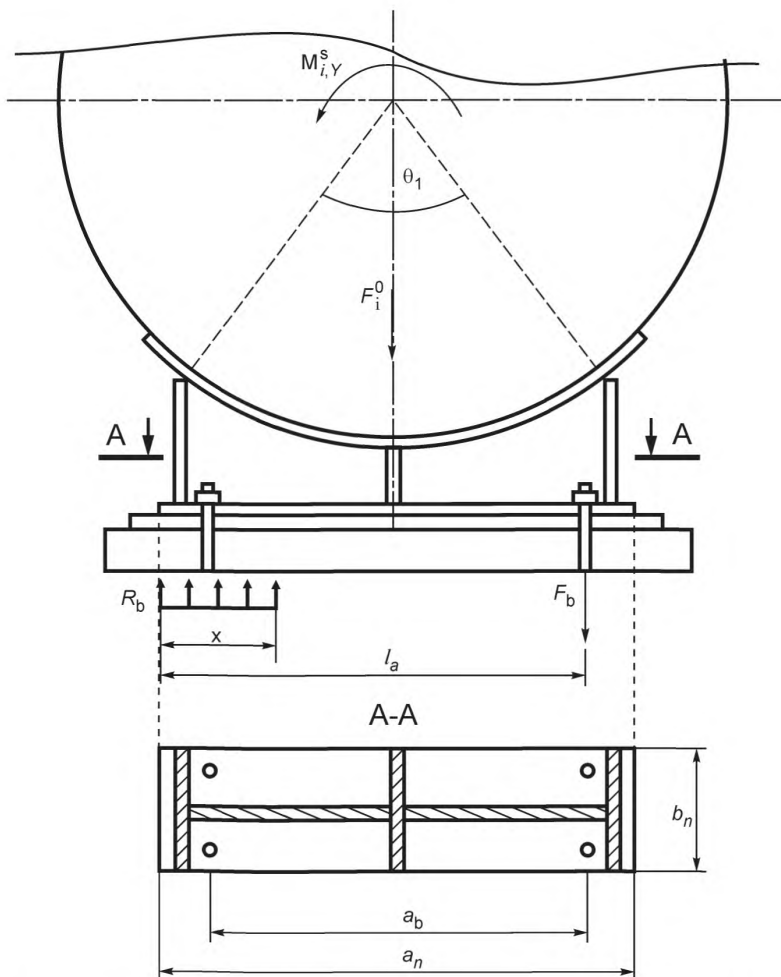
Расчетная схема для определения нагрузки на анкерные болты
